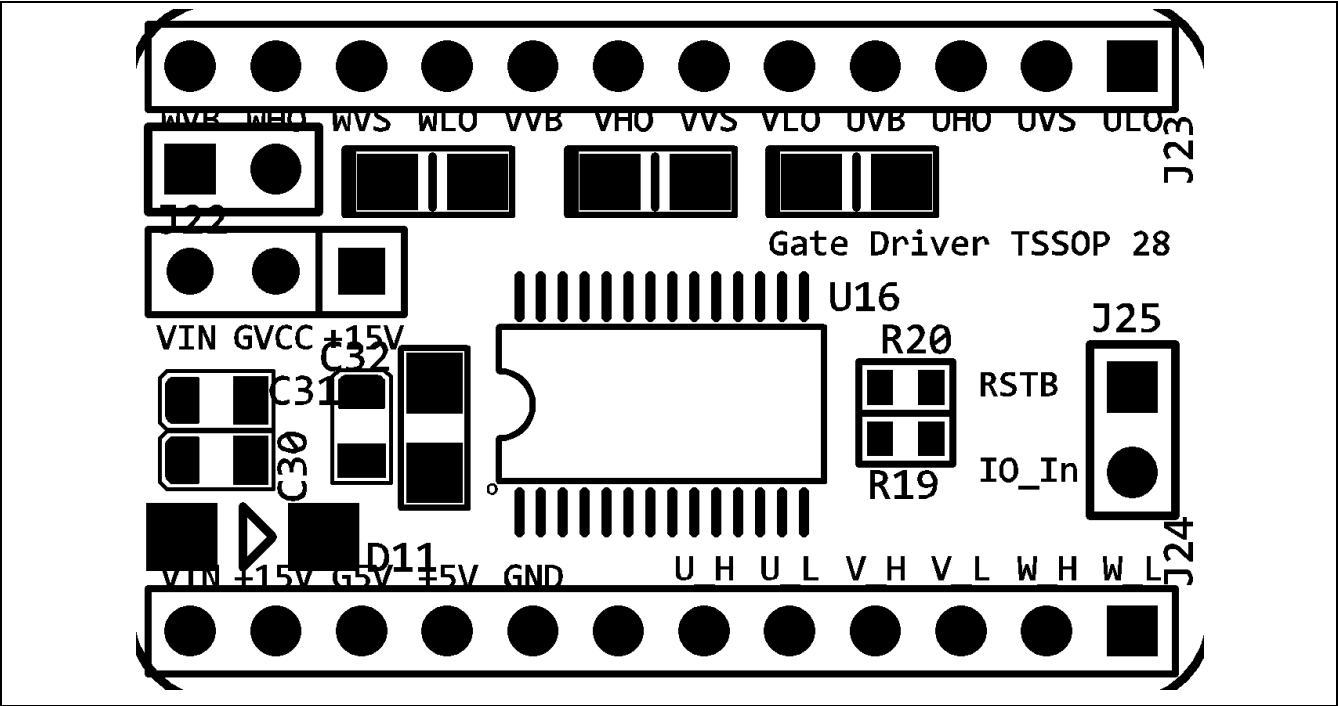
Gate Driver NCT3605 PCB 佈局-正面
